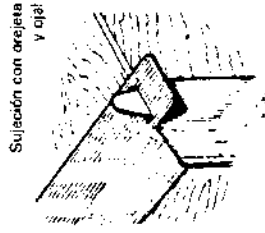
Caja de madera contrachapada, refuerzo metálico de las aristas
